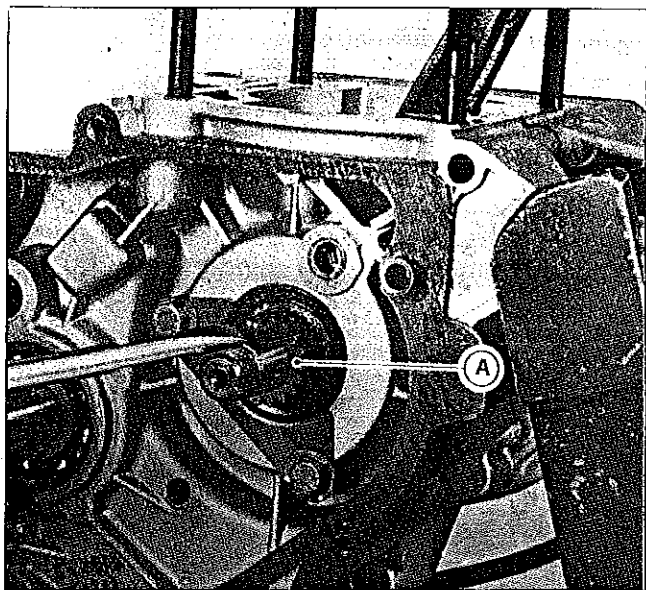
A. ENGRENAGEM COND. BOMBA DE ÓLEO
